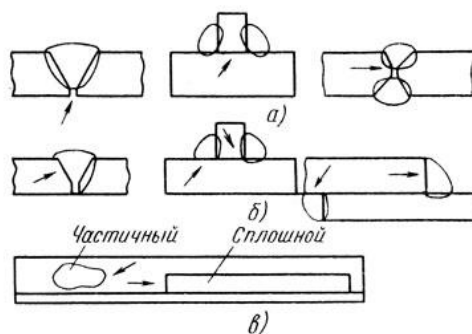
Непровары: а - корня шва, б - зоны сплавления, в - частичный и сплошной
